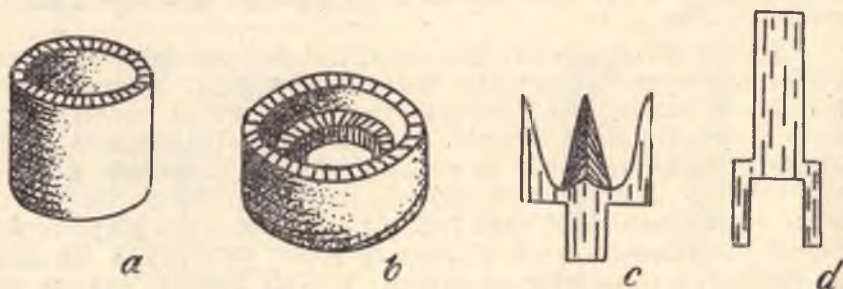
Aparatul de ștanțat coroane: a — chiuveta; b — inelul; c — dispozitivul pentru fracturarea aliajului ușor fuzibil; d — dornul
